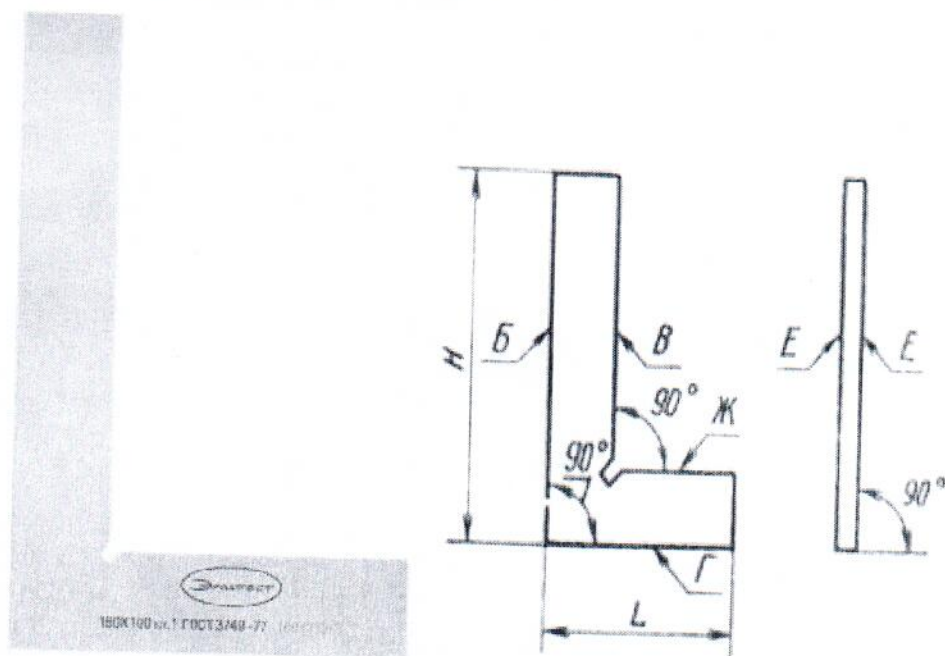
Общий вид угольника слесарного плоского 90° УП «Элитест», обозначение основных размеров и поверхностей
